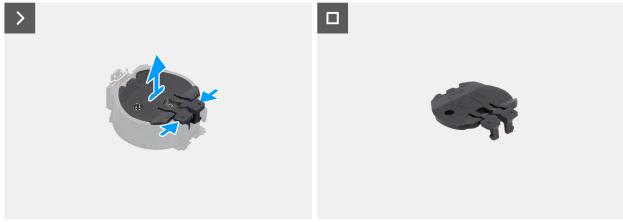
Extracción de la cubierta de la batería de tipo botón
